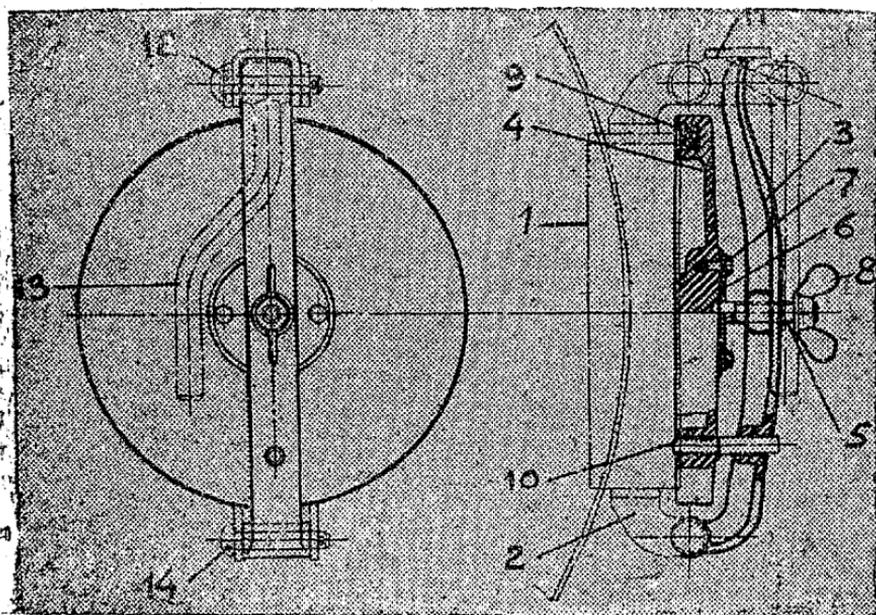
Крышка зольникового люка газогенератора в сборе: 1—горловина; 2—ушко горловины; 3—траверса крышки; 4—крышка; 5—упорный винт крышки; 6—шайба упорного винта крышки; 7—болт шайбы упорного винта; 8—барашек упорного винта крышки; 9—прокладка крышки; 10—установочная шпилька траверсы; 11—серьга запорного рычага крышки; 12—палец серьги; 13—запорный рычаг крышки; 14—палец запорного рычага крышки.
